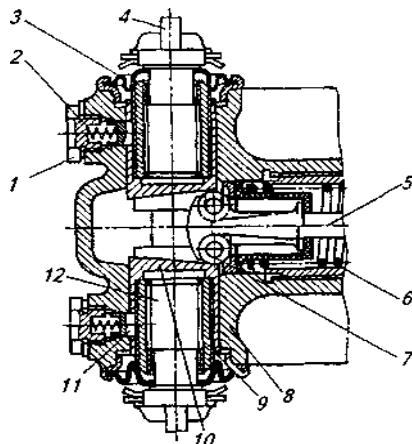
Клиновое разжимное устройство автомобиля КАЗ-4540 с автоматической регулировкой зазора: 1 — пробка; 2 — пружина; 3 — грязезащитный колпак; 4 — тормозная колодка; 5 — клин; 6 — пружина; 7 — ролик; 8 — суппорт; 9 — регулировочная втулка; 10 — толкатель; 11 — штифт-храповик; 12 — регулировочный винт
